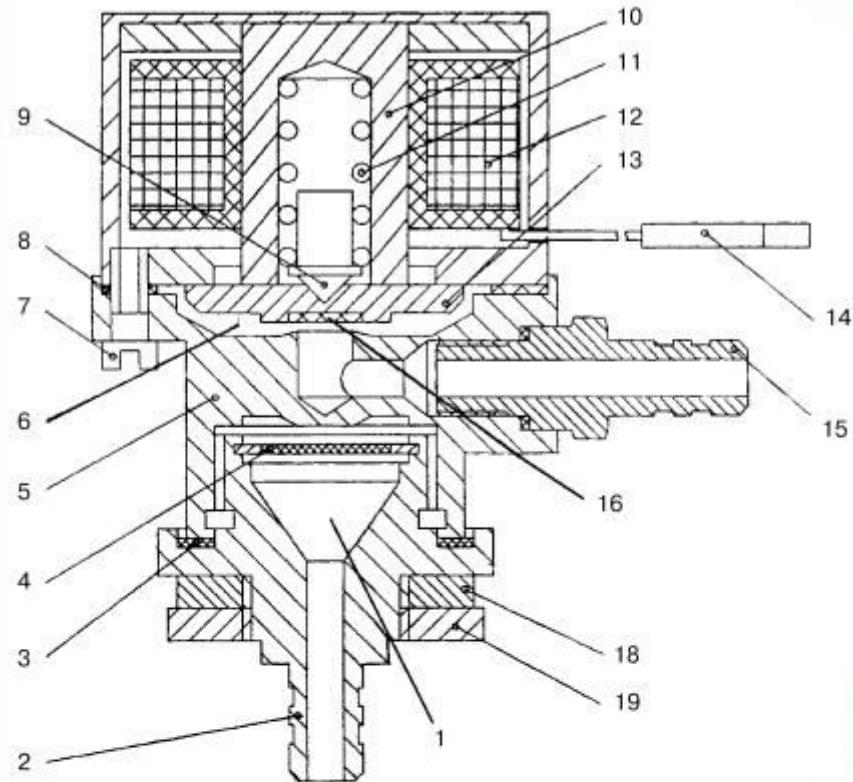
Электромагнитный клапан «САГА-6»: 1 – входная полость; 2, 20 – штуцер; 3, 8 – уплотнительные прокладки; 4 – фильтр; 5 – корпус; 6 – выходная полость; 7 – винт крепления; 9 – центрирующий толкател; 10 – корпус электромагнита; 11 – пружина; 12 – катушка электромагнита; 13 – запорная шайба; 14 – вывод обмотки катушки электромагнита; 15 – выходной штуцер; 16 – уплотнитель; 17 – газовый штуцер; 18 – кронштейн крепления;
